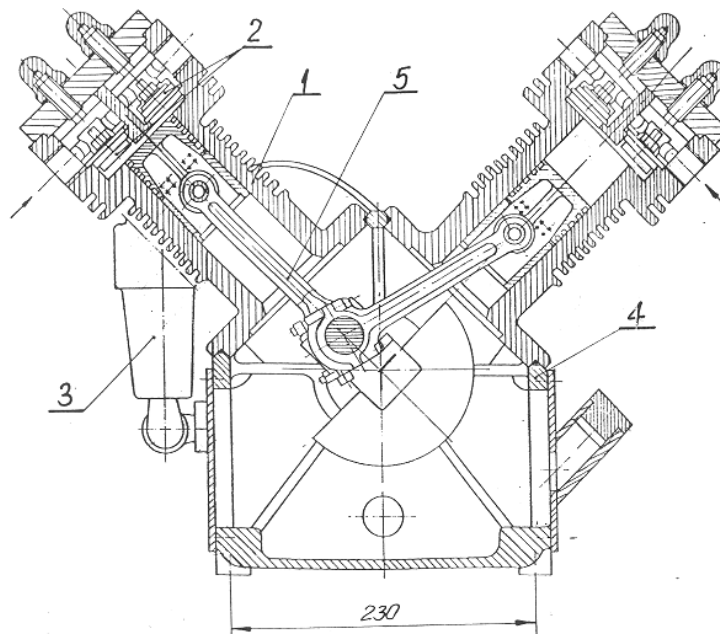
Перерезь главный компрессора V1.5.V Бустер ADP 300-150
